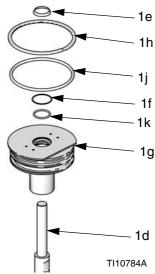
Joint de tige de piston de 165,1 mm (6,5 po.)
